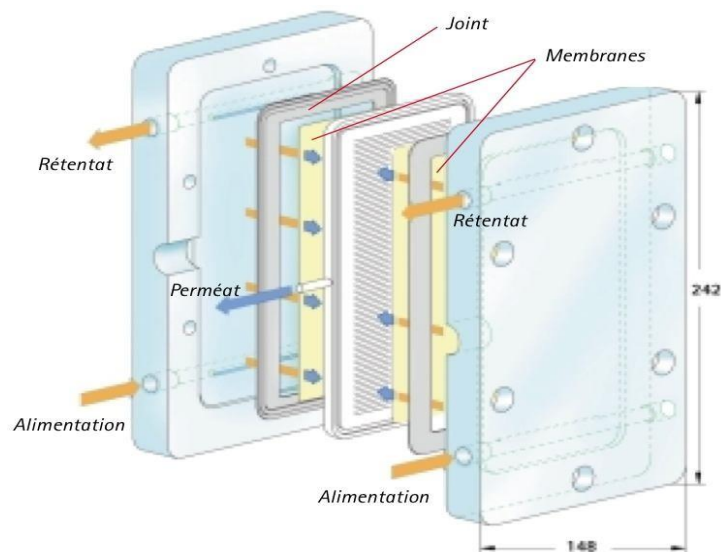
Schéma du module plan Ray-Flow X 100.
